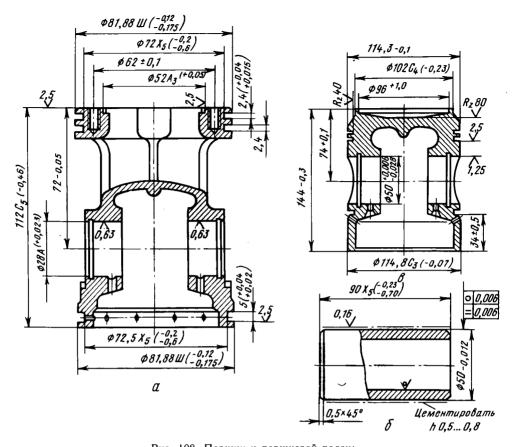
Поршни и поршневой палец: a — поршень прямоточного компрессора AУ45;  $\delta$  — поршневой палец;  $\delta$  — поршень непрямоточного компрессора П110
